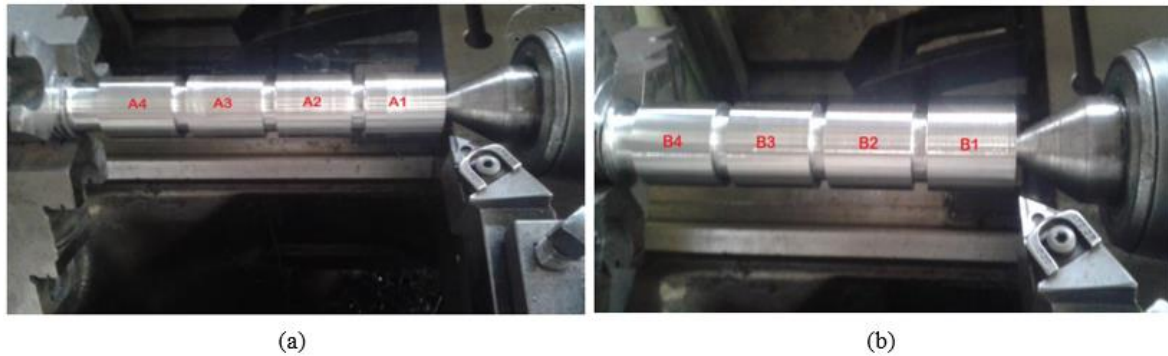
(a) Corpos de prova usinado com inserto de raio de ponta de 0,8 mm. (b) Corpos de prova usinado com inserto de raio de ponta de 0,4 mm.
